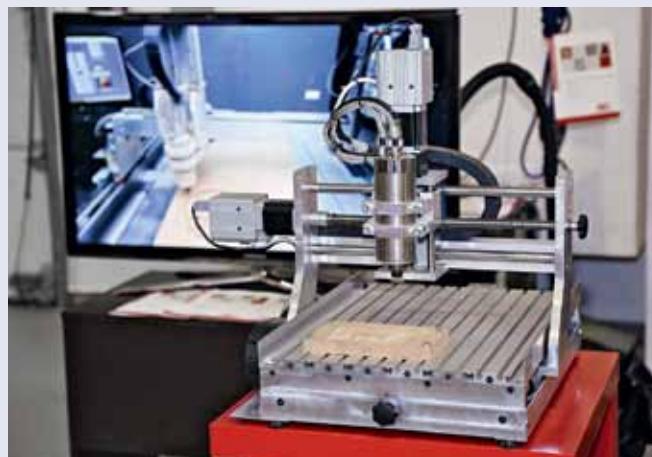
Фрезерно-гравировальный станок АТС-400 на международной выставке "Металлообработка-2015"
